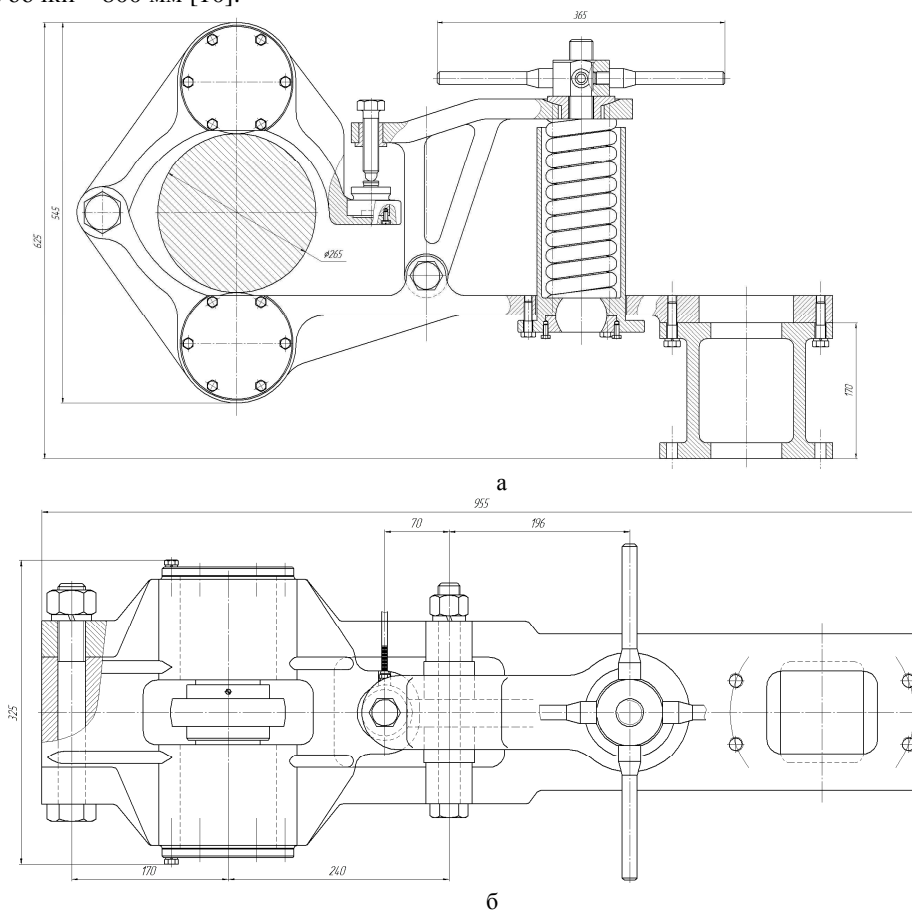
Устройство для обкатки валков диаметром от 193 до 265 мм: а - главный вид, б - вид сверху
